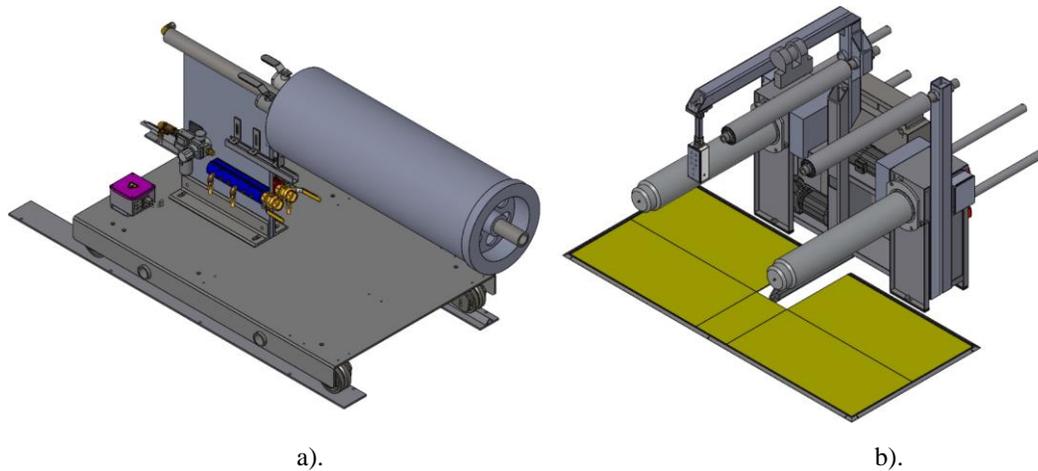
Modelos: a). Mandril de enfriamiento y moldeo. b). Bobinadora *Winder*.
